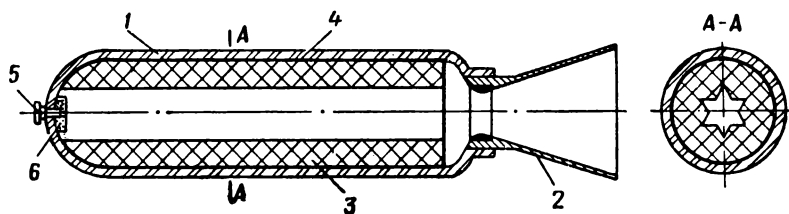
Схема ракетного двигателя на твердом топливе с зарядом, скрепленным со стенками ракетной камеры:
